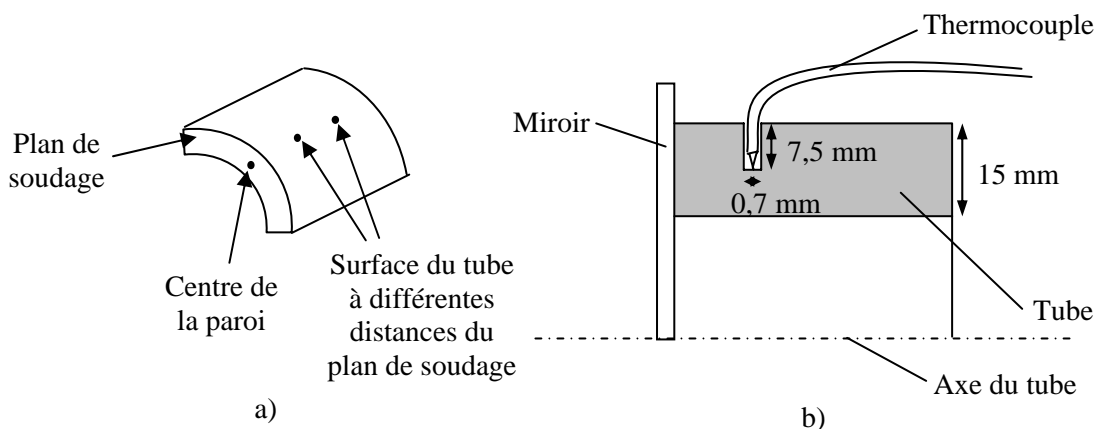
a) Quelques points de mesures de température dans le tube ; b) Implantation des thermocouples au centre de la paroi du tube (vue en coupe)
